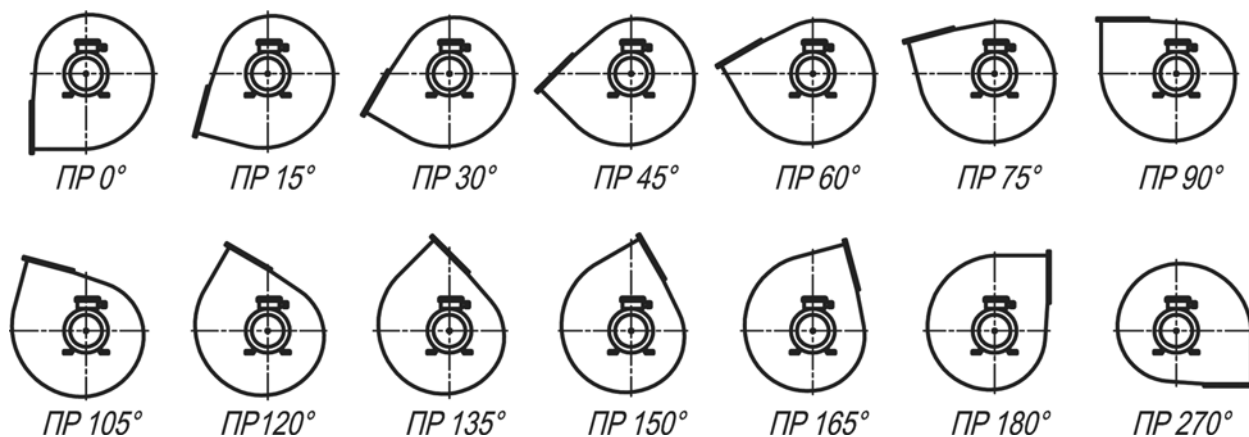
Положение корпуса тягодутьевых машин типа ВД и Д.
